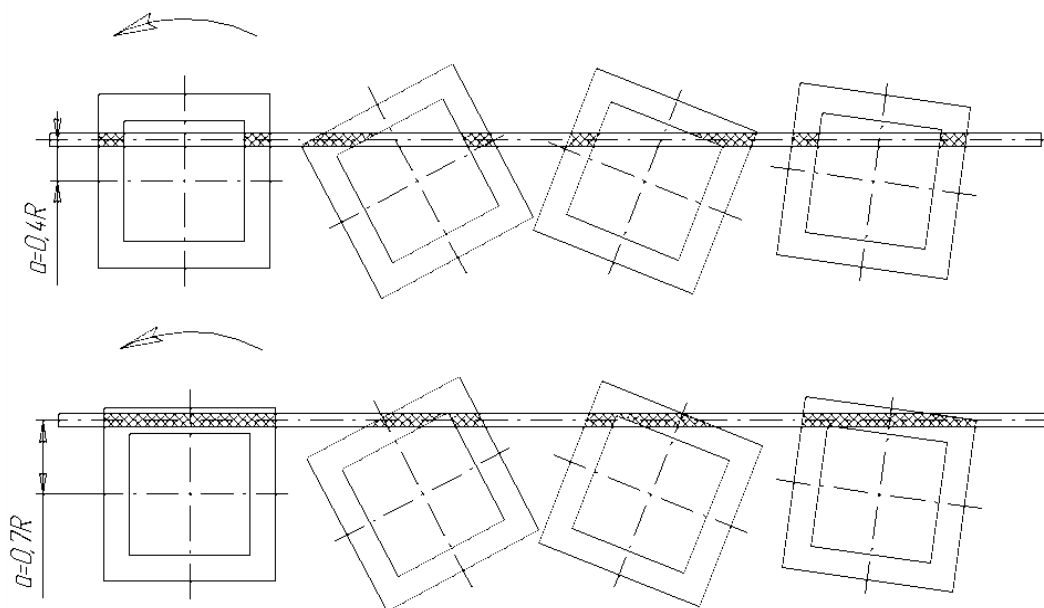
Формирование «осциллирующего» пятна контакта инструмента с некруговой рабочей поверхностью и цилиндрической детали:
